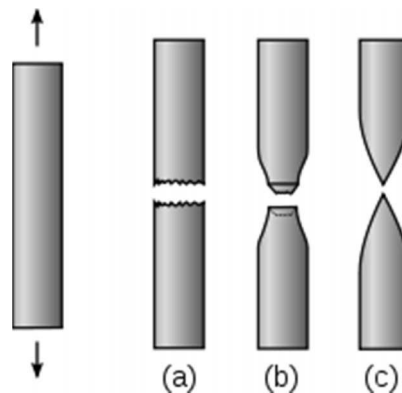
17 Tipos de fractura más comunes en ensayos a tensión. A) fractura totalmente frágil. B) Fractura de copa y cono y C) fractura totalmente dúctil.
